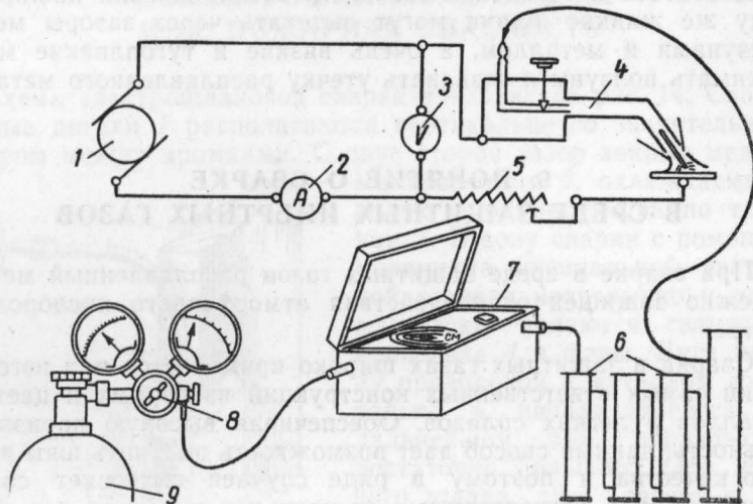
Схема установки для аргоно-дуговой сварки на постоянном токе
